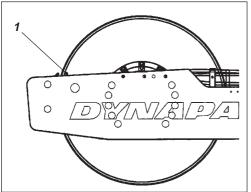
Lato del tamburo sinistro 1. Indicatore
